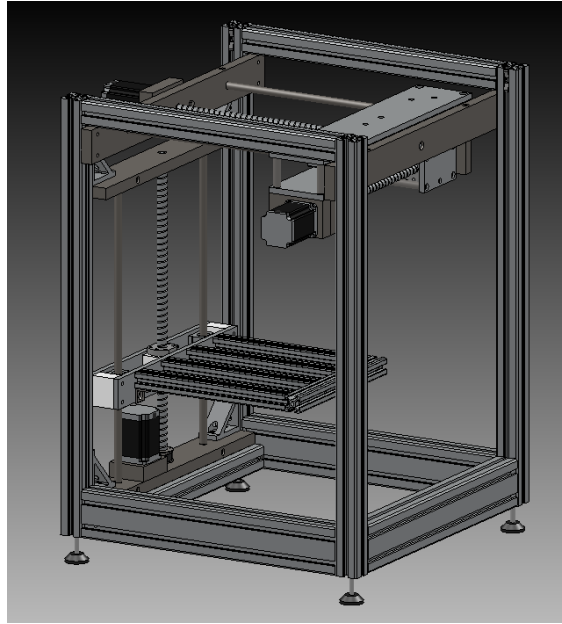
Diseño mecánico del manipulador cartesiano.
